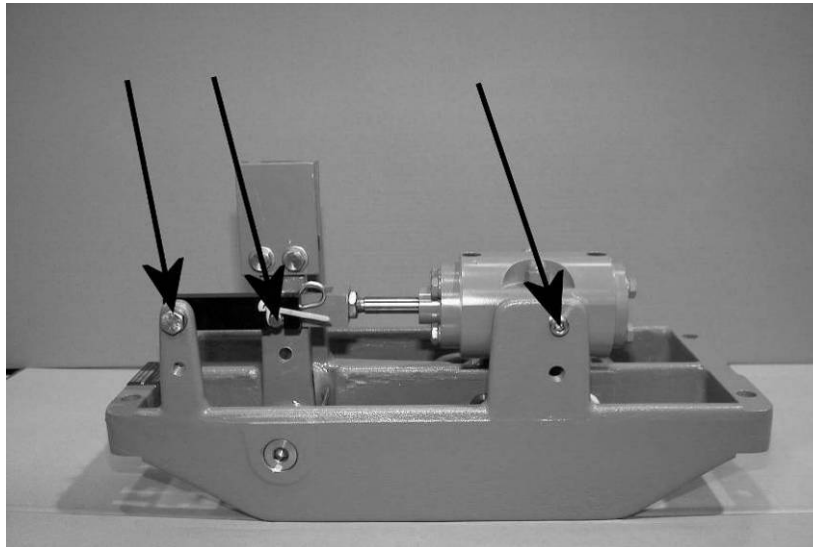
Montowanie sworzni gwintowanych pakietu sprężyn
